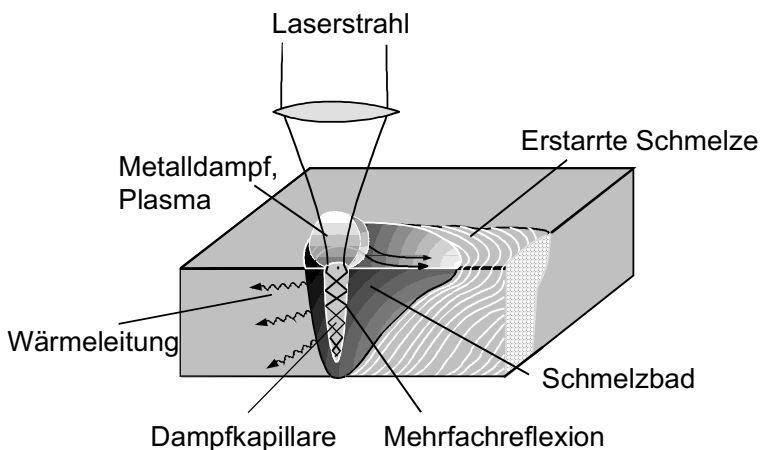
Physikalische Mechanismen des Lasertiefschweißens.
